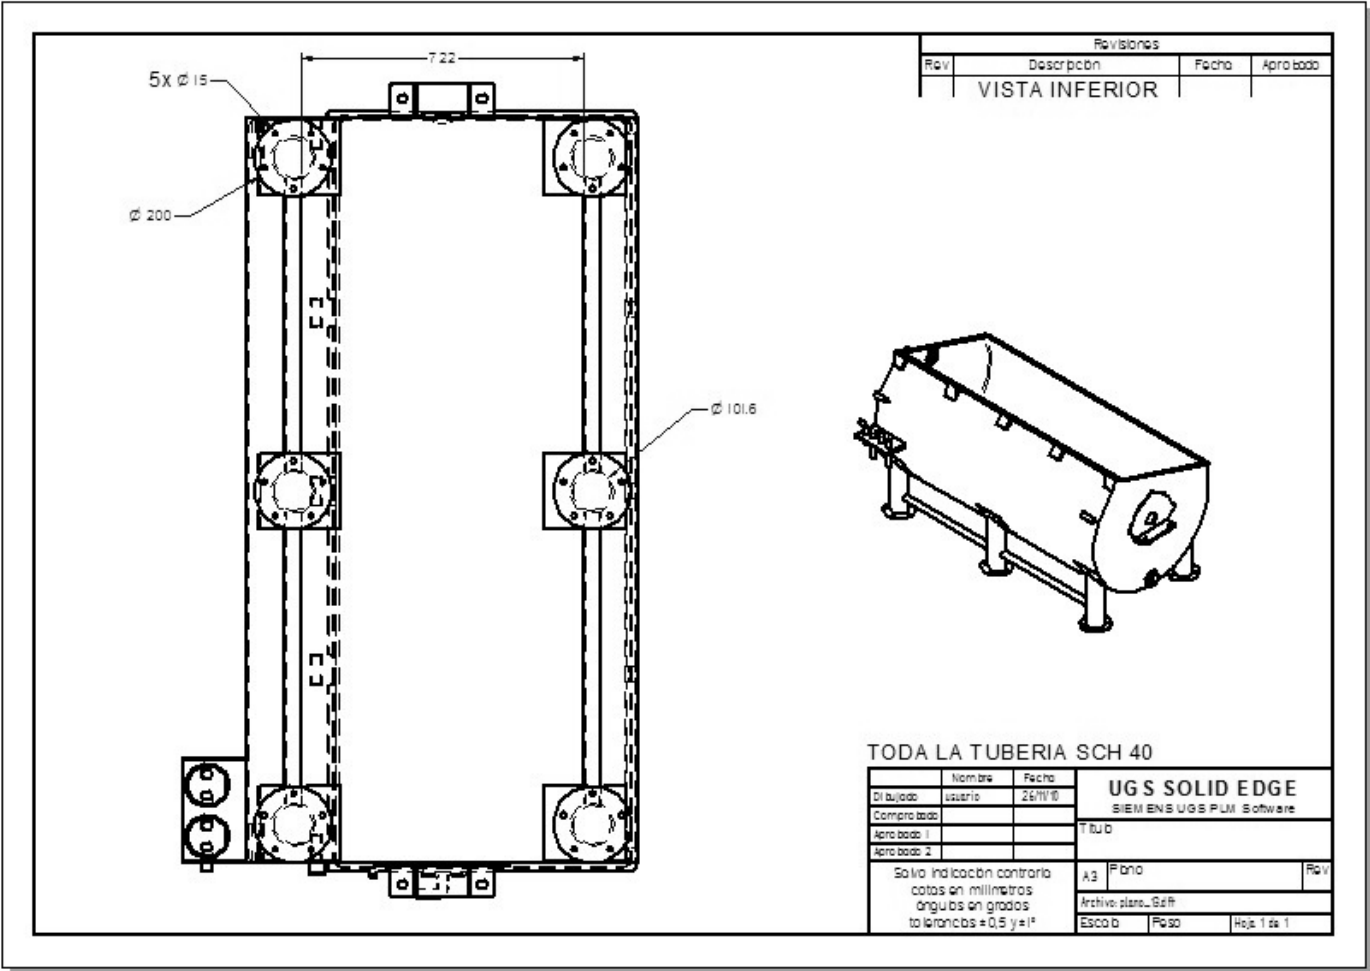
Plano del contenedor de mezclado, vista inferior, detalle 9.
